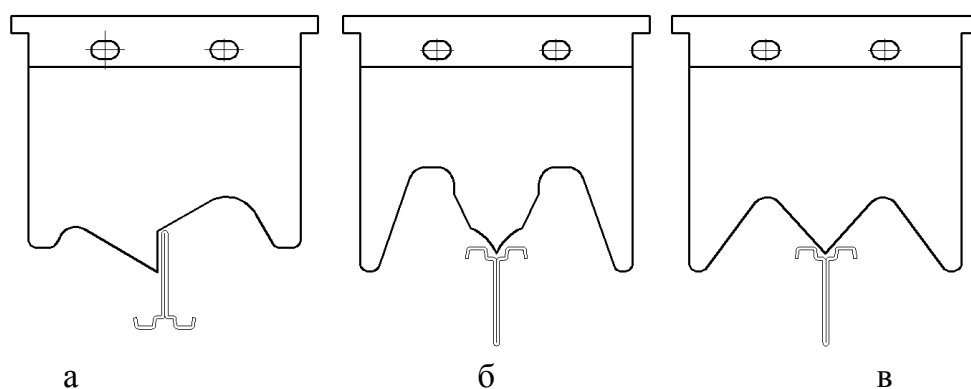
Варианты ножей для резки в штампе стандартным способом: а – нож со смещенным центром реза, б – нож конусный копьевидный, в – нож конусный
